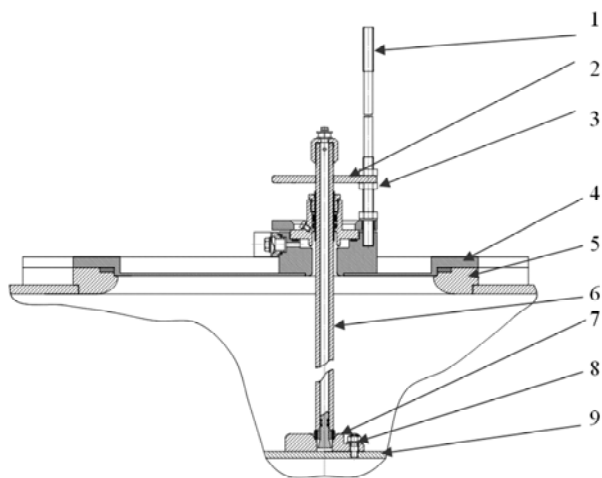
Конструктивное изображение закоротки (исходное положение) с ручным управлением: 1 – шпилька; 2 – направляющая; 3 – гайка М12; 4 – крышка; 5 – крышка ГИН; 6 – шток; 7 – фланец; 8 – шпилька; 9 – шина
